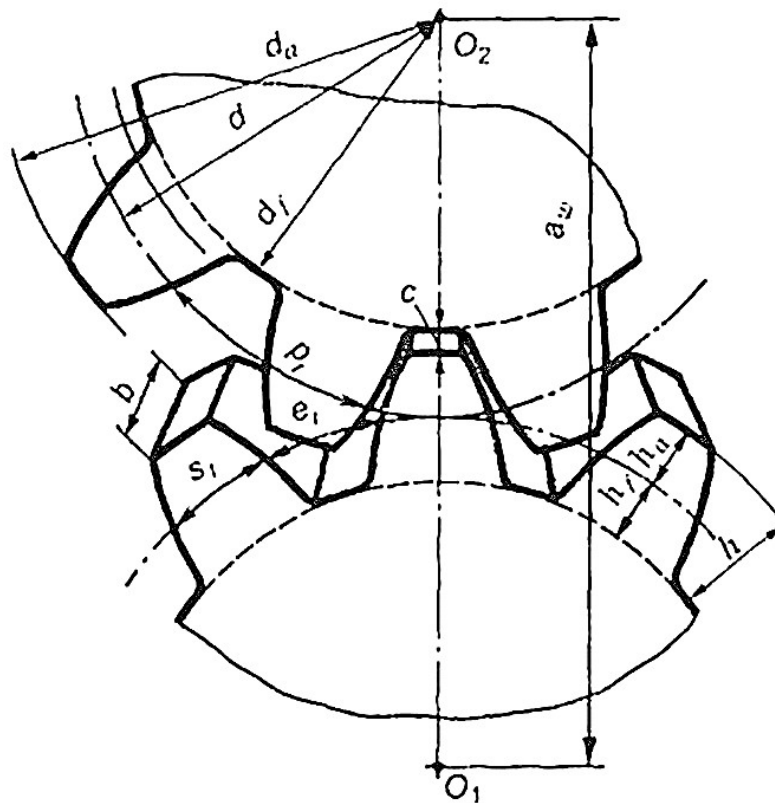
Геометрические параметры цилиндрической зубчатой передачи
